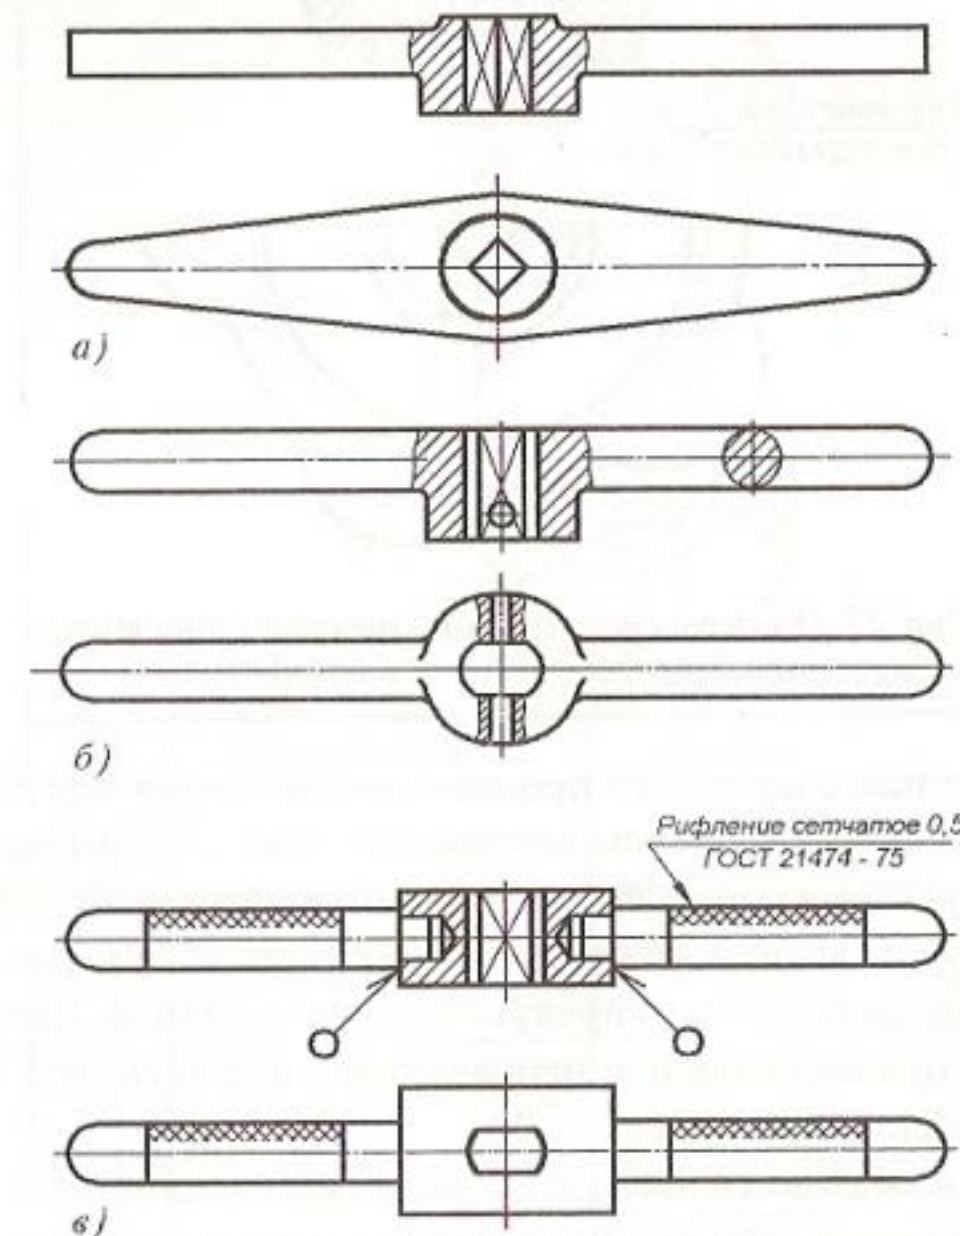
Примеры конструкций рукояток-воротков: а – плоские; б – круглые; в – вороток в виде сборочной единицы.
